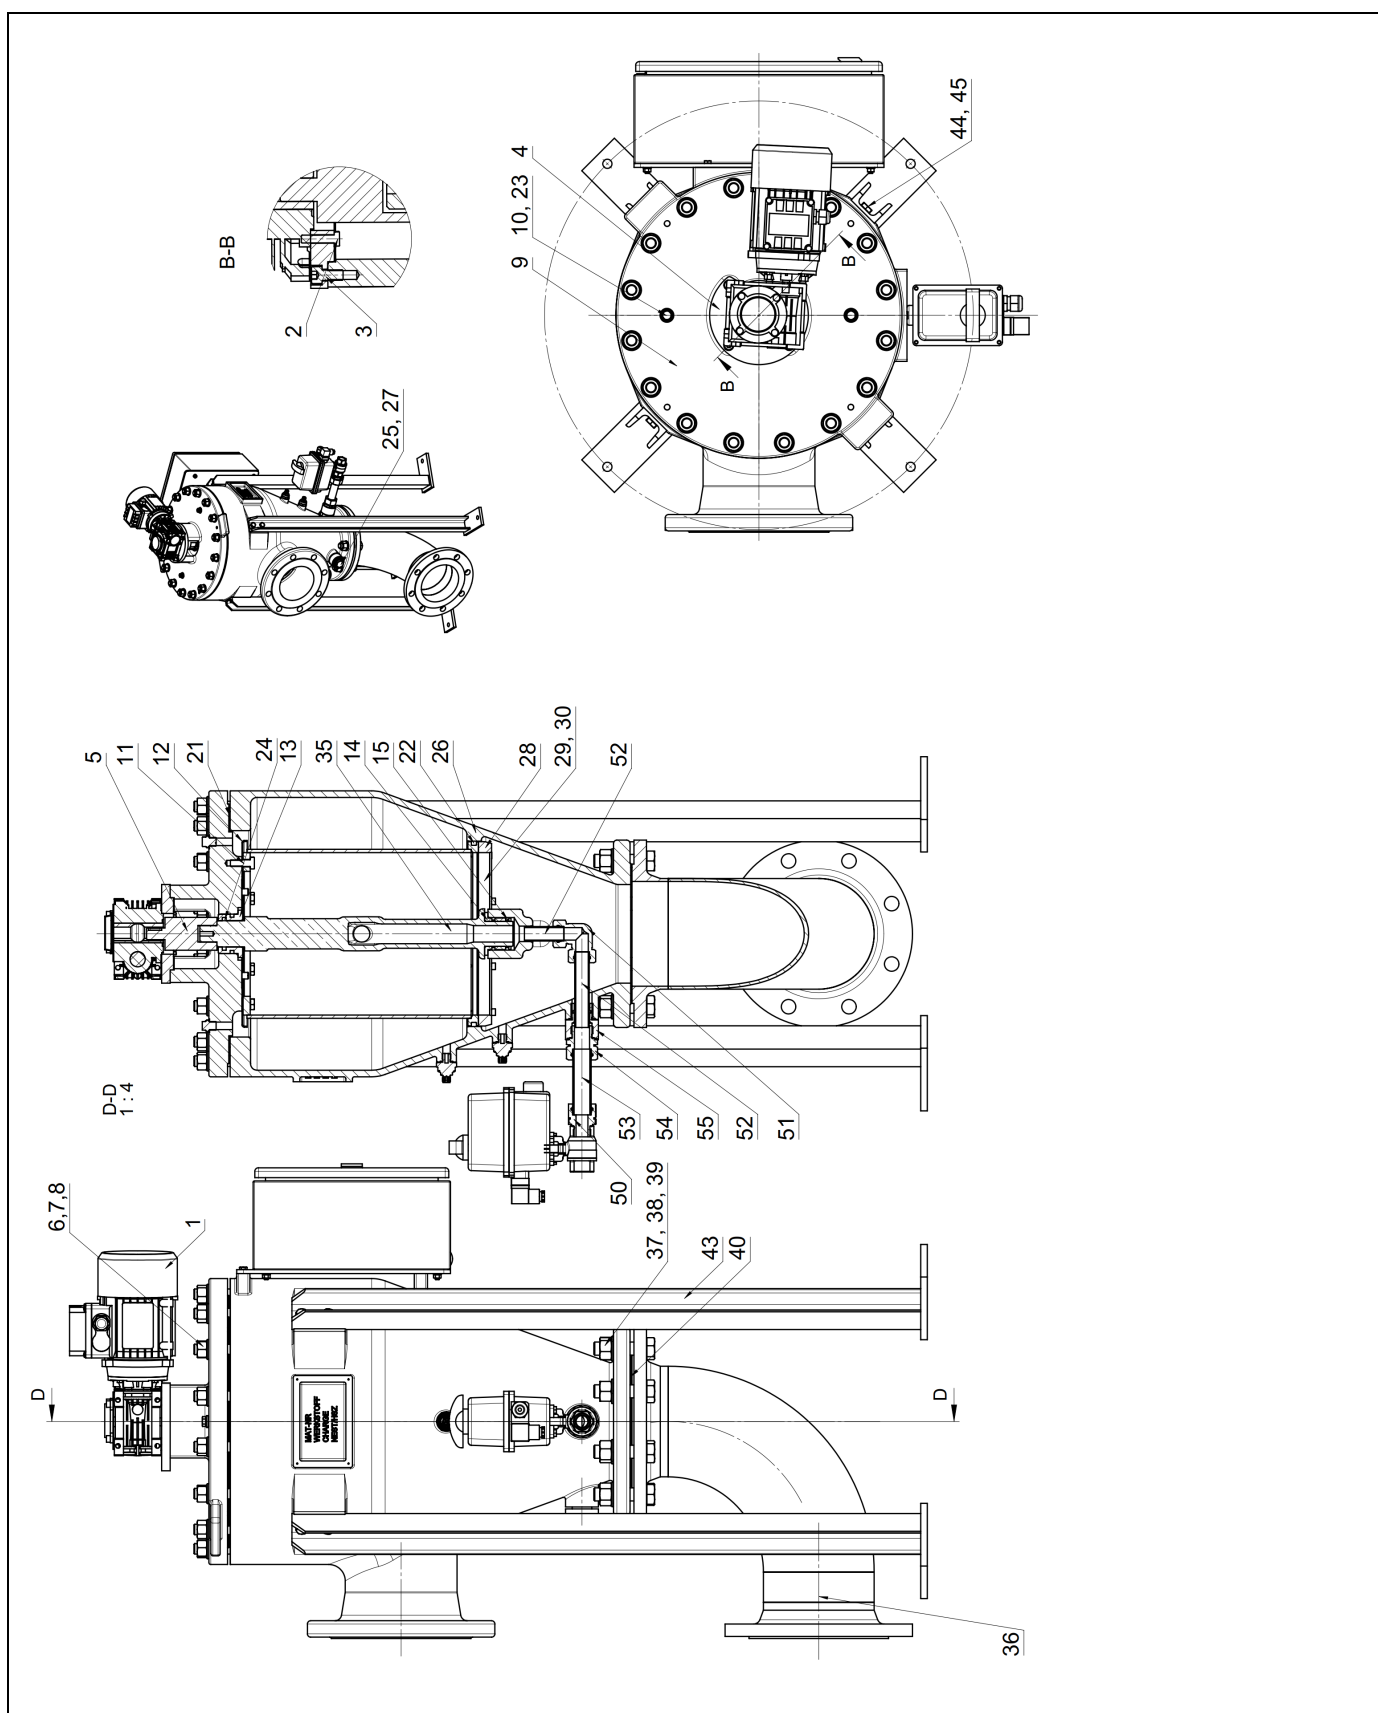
Dessin de pièces de rechange R8-80 Position de bride 1
